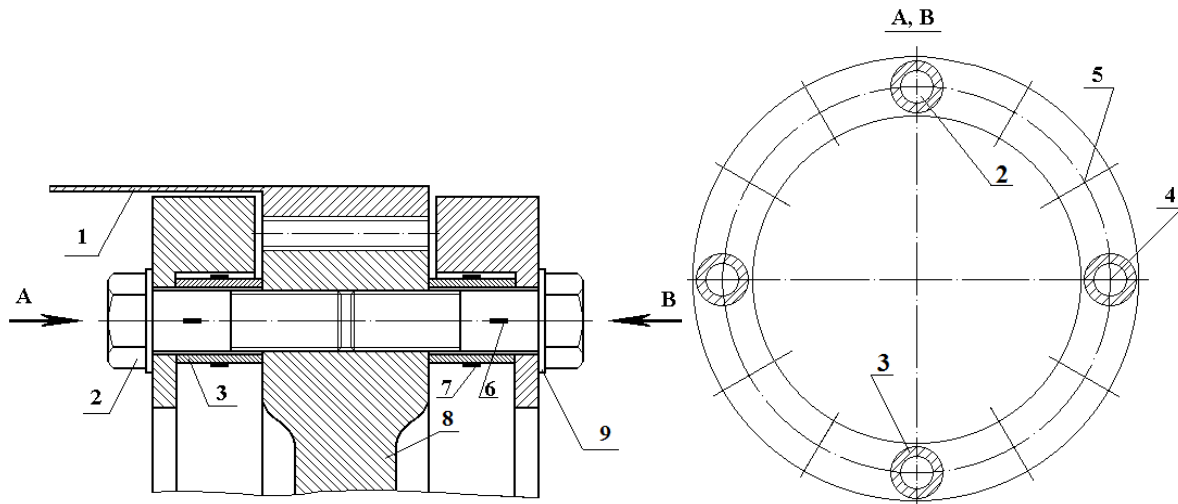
Сопряжение гибкого колеса со ступицей выходного вала редуктора:
